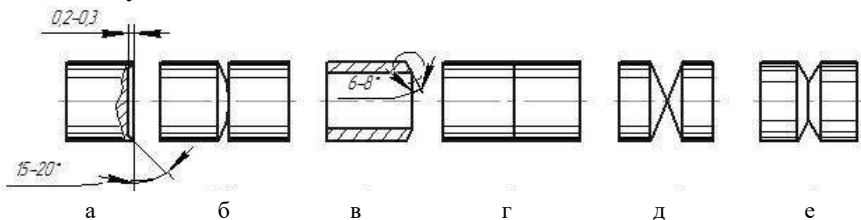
Форма торців зварюваних заготовок при зварюванні опором
